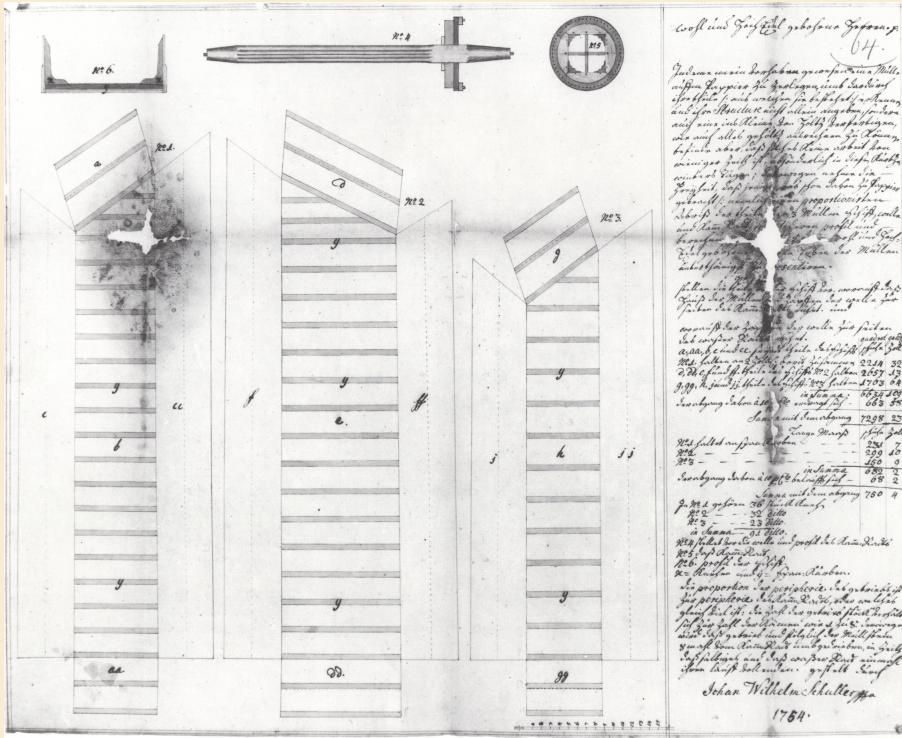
Bauplan einer Rheinmühle, drei Mühlenscheiffe, Welle, Kammrad.
